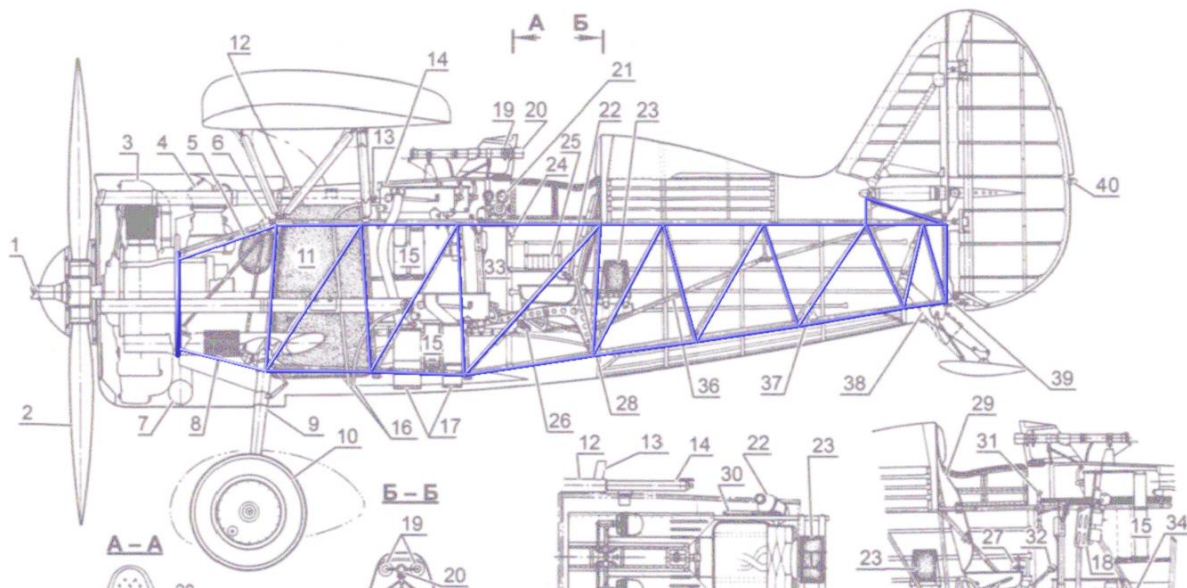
Perfil de la estructura modelada sobre el plano escalado
